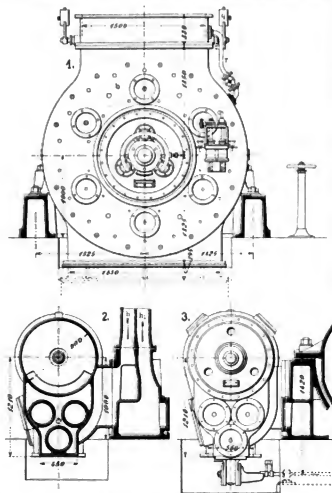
Z. A.: Zerstüßungs-Hochexpansions-Gebläsmaschine.
